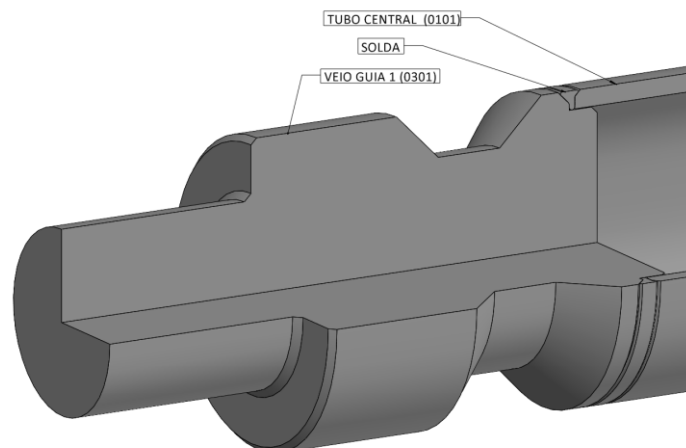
Representação da solda utilizada no estudo do rolo mandante.
